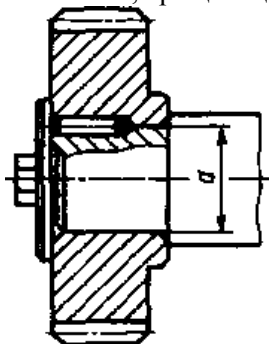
Штифтовое соединение зубчатого колеса с валом
